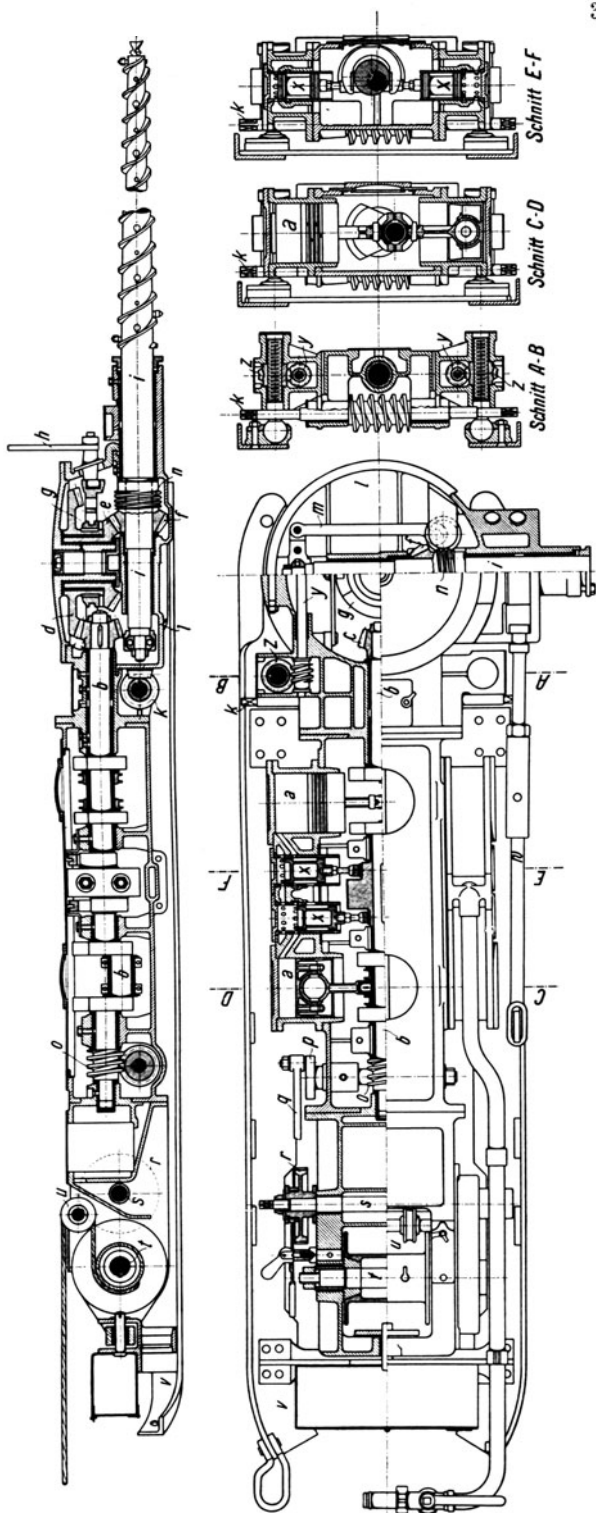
Schwere Schrämmaschine mit vierzylindrigem Kolbendruckluftmotor.
